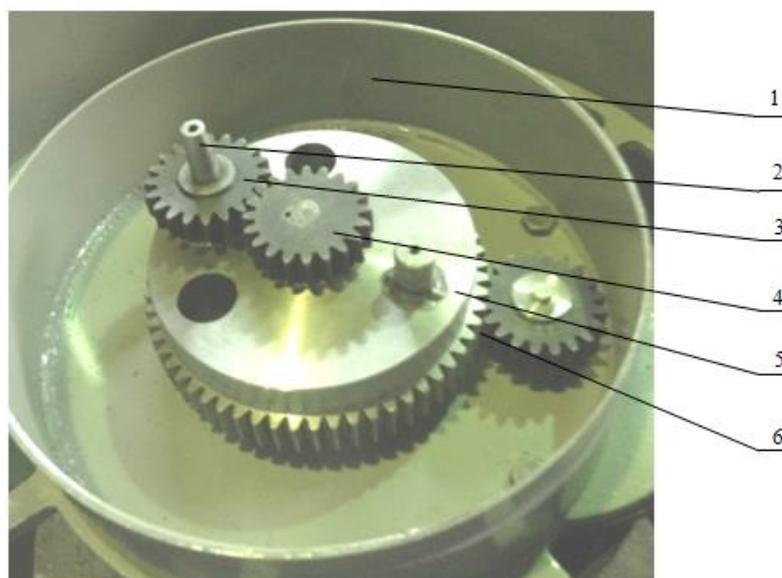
Механизм привода нижнего диска: 1 – корпус привода; 2 – вертикальный вал; 3 – сателлит; 4 – опорное зубчатое колесо; 5 – водило; 6 – зубчатая передача привода водила
